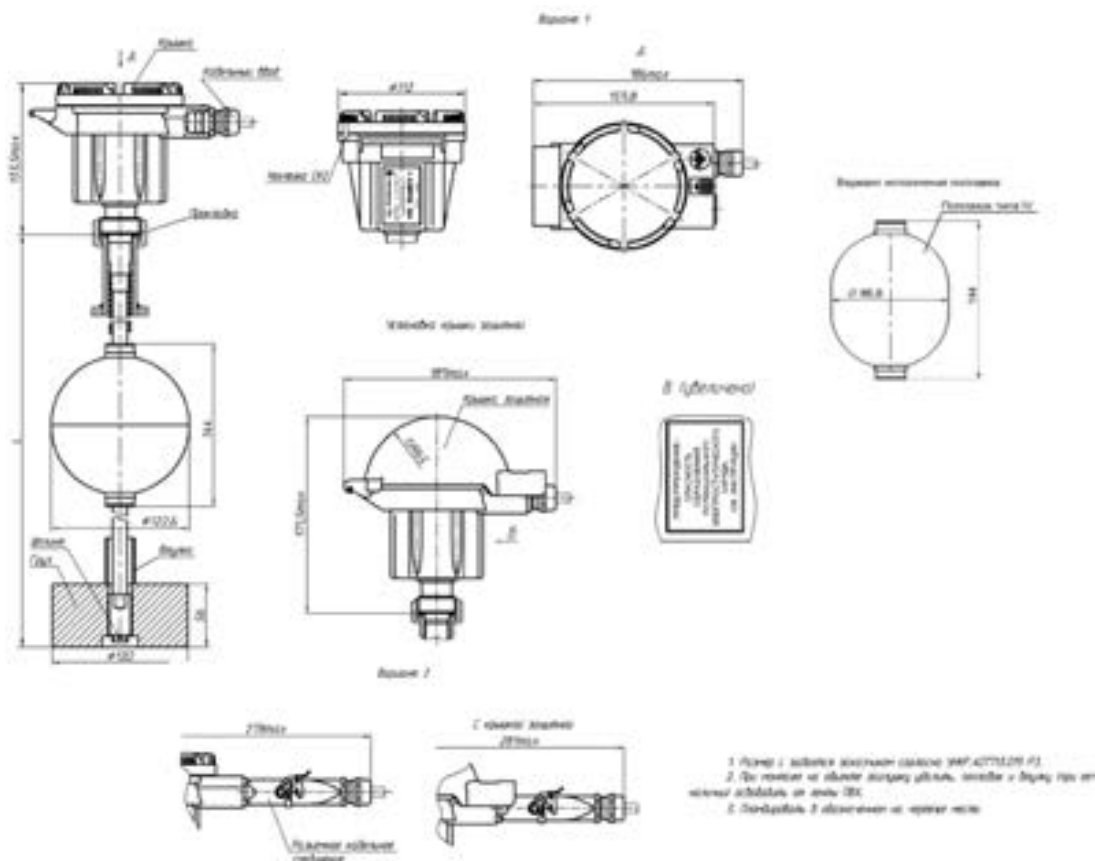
Габаритные размеры датчика ДПУ8М
